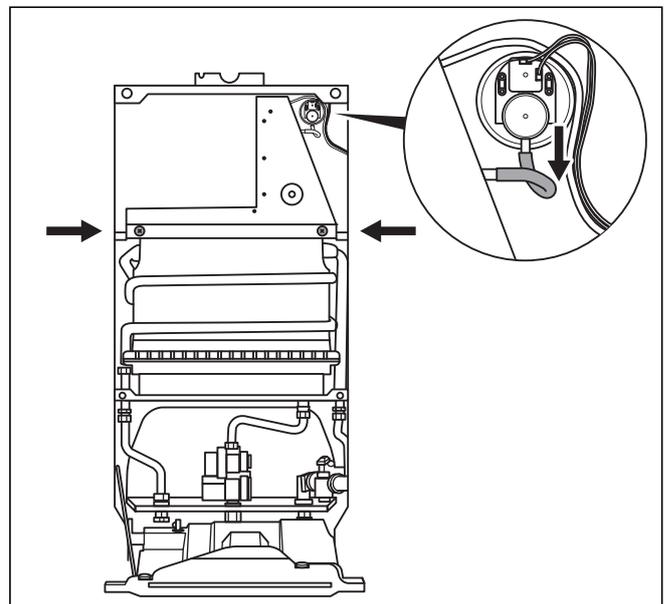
Démontage du capot collecteur de produits de combustion (Fig. : type 17-2/O)
